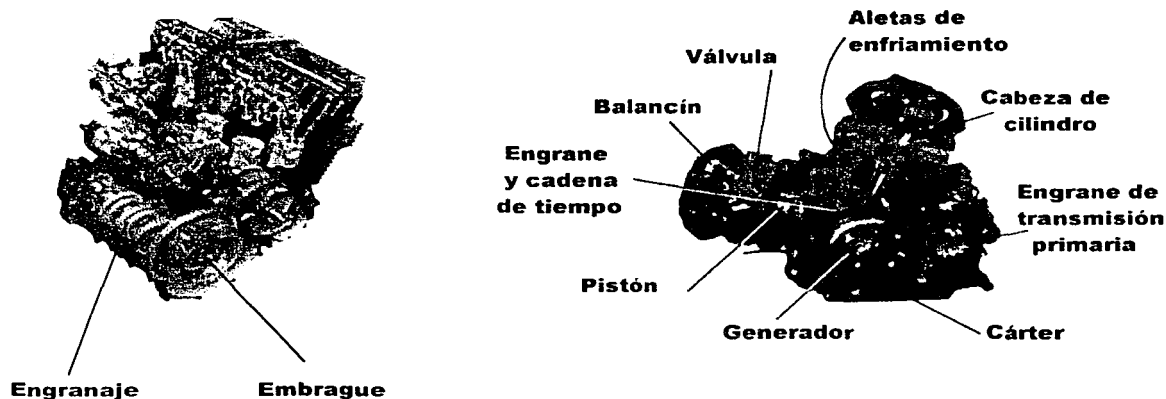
Motor tetracilíndrico en corte que muestra los engranes de transmisión primaria, con velocidades y embrague. Figura 4.18; corte de un motor Ducati 907 bicilíndrico en V a 90o.
